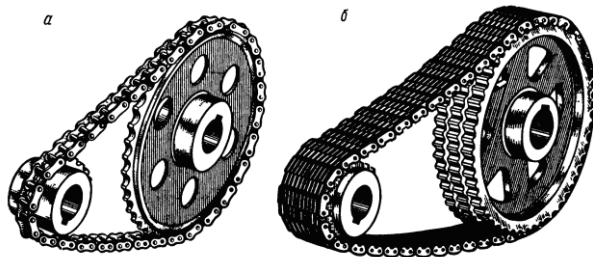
Цепная передача: а – роликовая; б – зубчатой цепью
